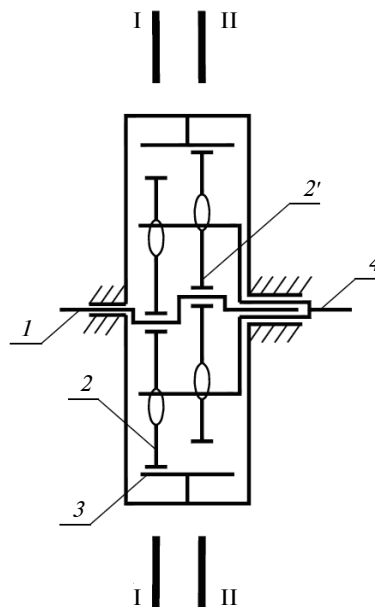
Структурна схема редуктора: 1 – ведуча ланка; 2, 2' – сателіти; 3 – корпус; 4 – вихідна ланка
